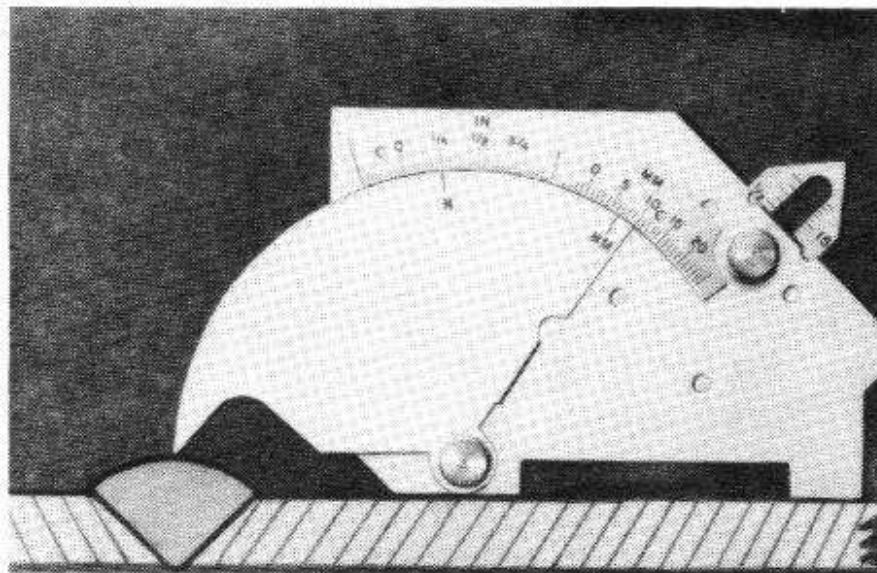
Medición de la sobremonta en el cordón de soldadura.
